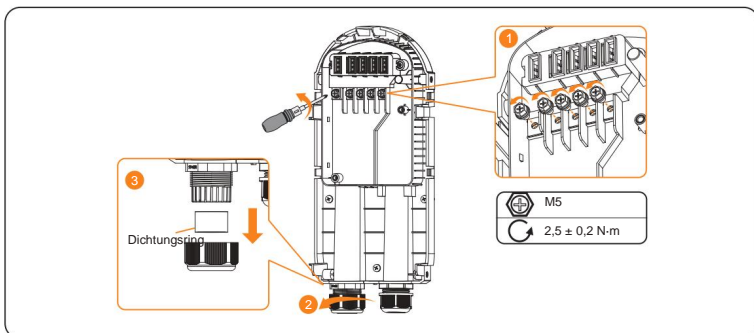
Schrauben entfernen und die Schwenkmutter lösen.
